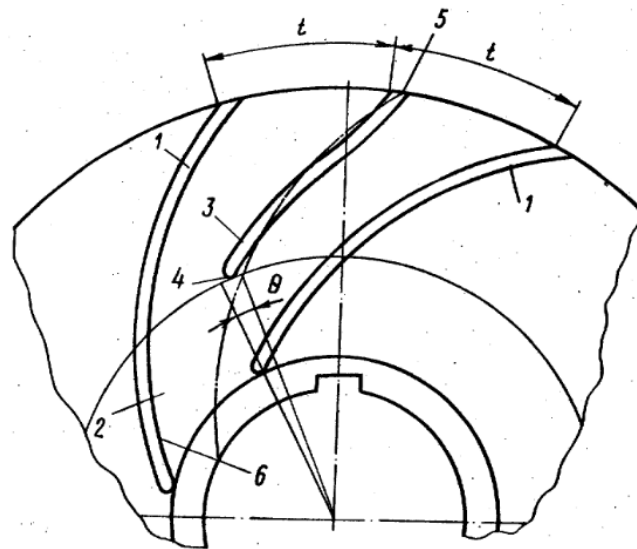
Двухъярусная решетка с S-образными короткими лопастями
